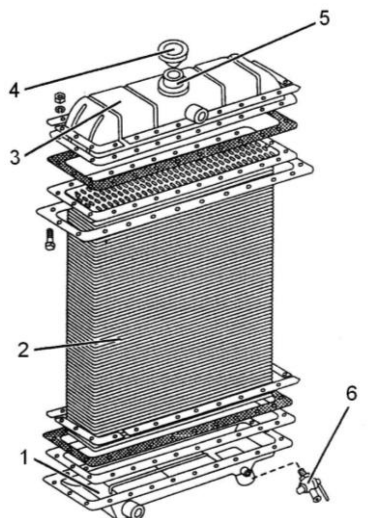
Радиатор трубчато-пластинчатый сборной конструкции:
